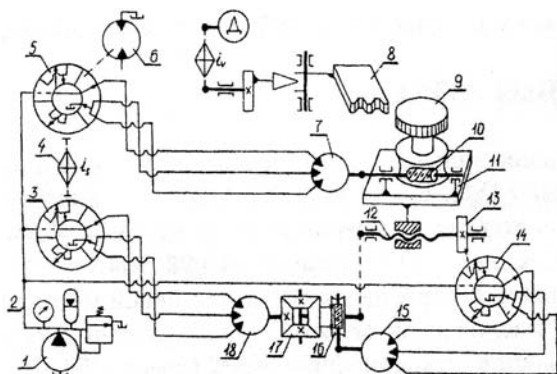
Структурная схема зубострогального станка с гидравлическими связями для нарезания цилиндрических зубчатых колес зуборезной гребенкой
